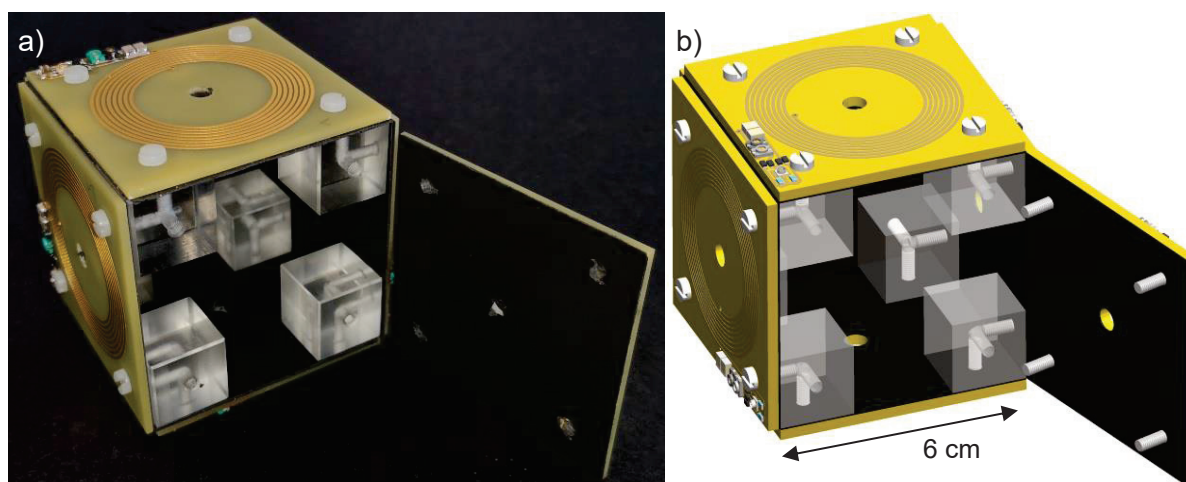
Assemblage du cube récepteur a) dispositif réel et b) CAO.
